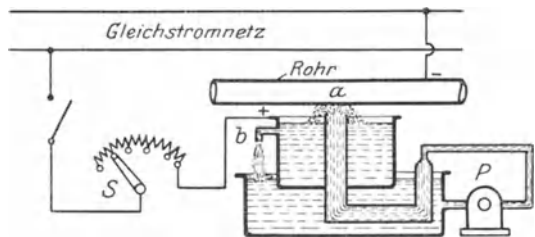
Schweißen einer Rohrlängsnaht durch Elektrolyse.
